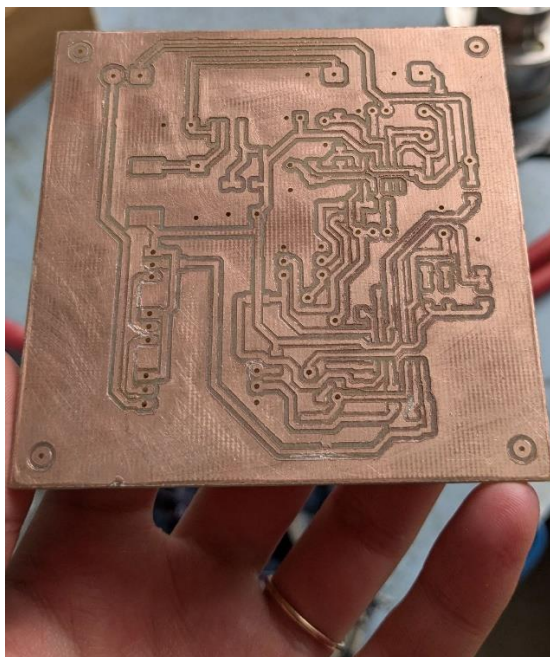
Готова плата, доріжки якої виконані фрезеруванням
